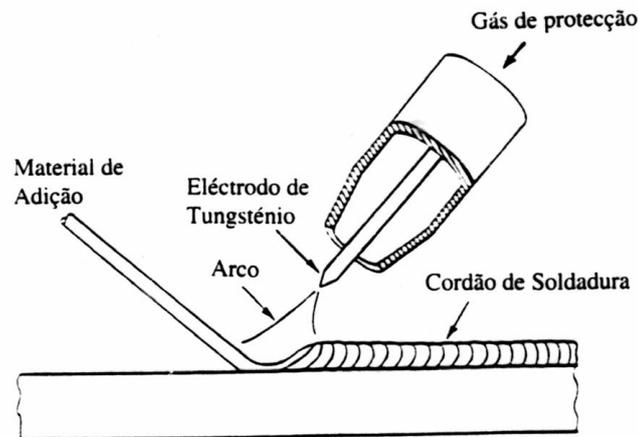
Esquema Representativo da Soldadura TIG [37]
